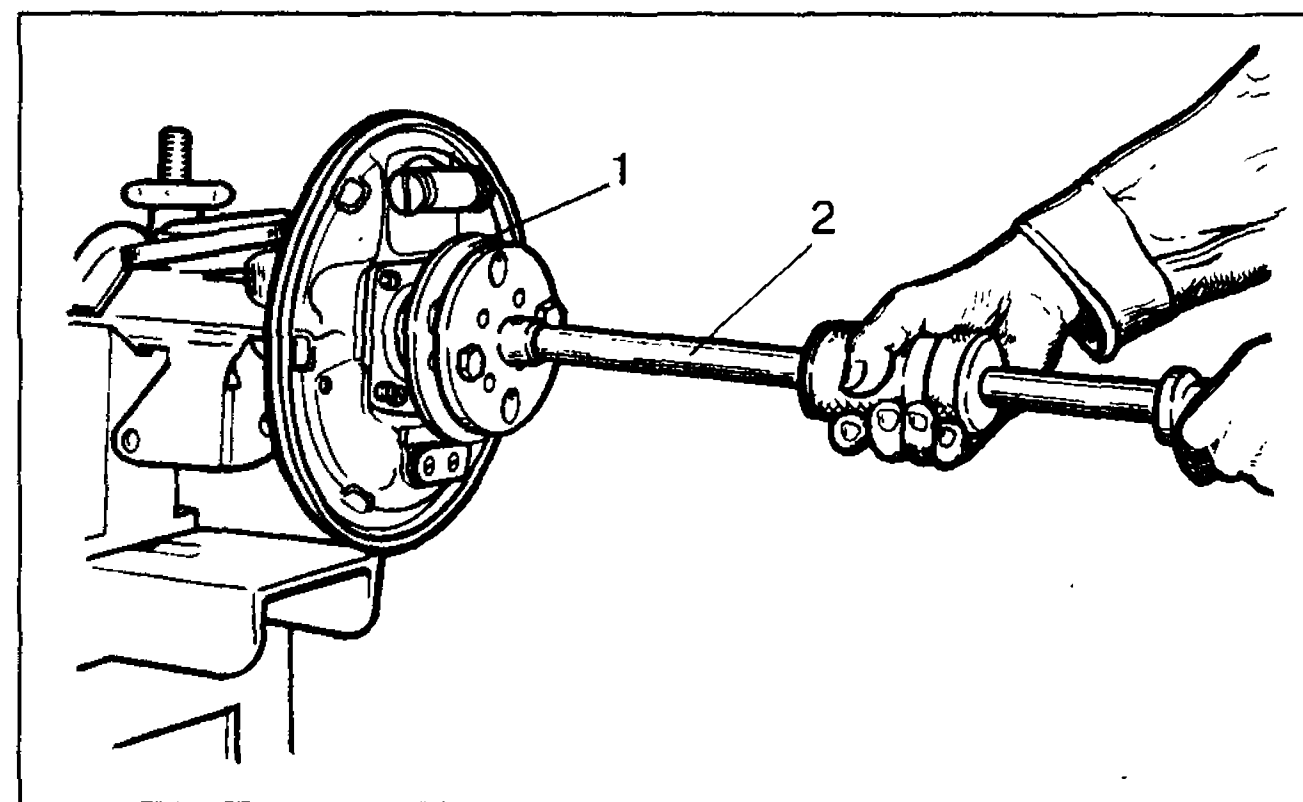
Выпрессовка полуоси с помощью съемника 67.7801.9516: 1-полуось; 2-ударный съемник
